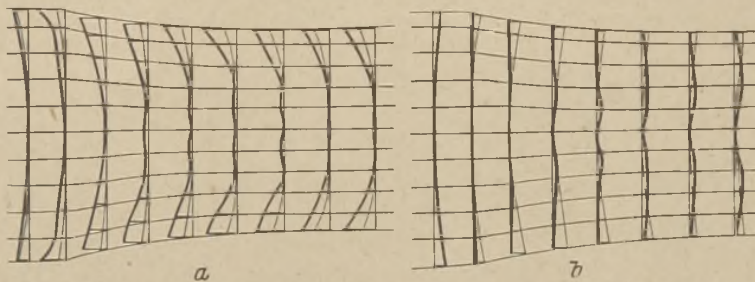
und b. Schiebungen an den Walzstäben nach zwei Stichen mit gleichbleibender (a) und wechselnder Walzrichtung (b). Stichabnahme 20%.
